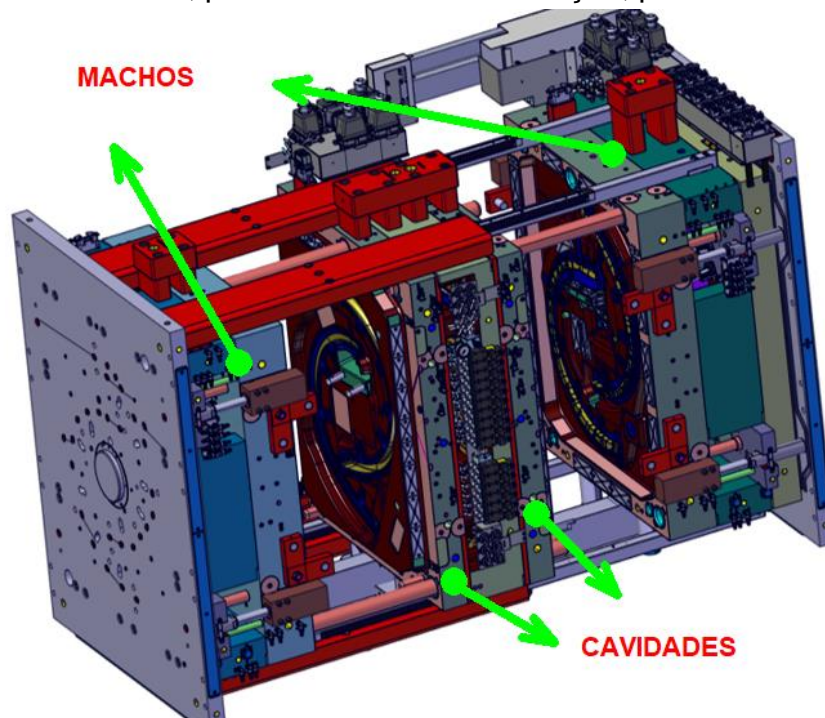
Exemplo de um molde *sandwich* fabricado na SF Moldes.
